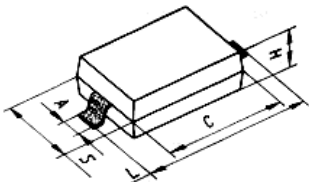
Корпуси SMA, SMB і SMC
